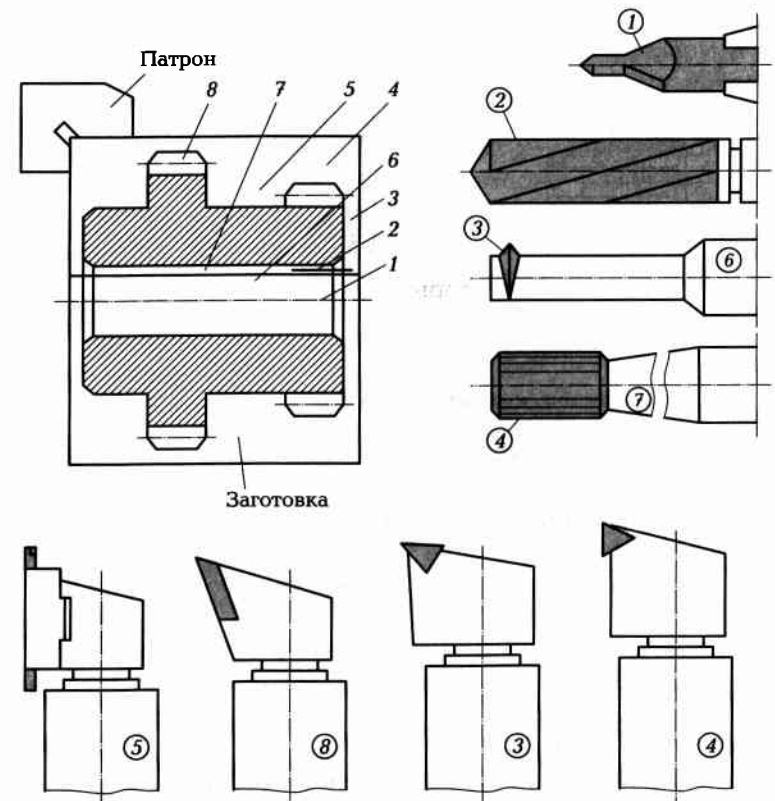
Схема обработки зубчатого колеса на токарно-револьверном станке с ЧПУ (номер инструмента соответствует номеру обрабатываемой поверхности)
